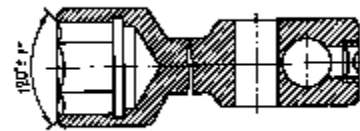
Ключ S=60 для гаек крышки цилиндров
